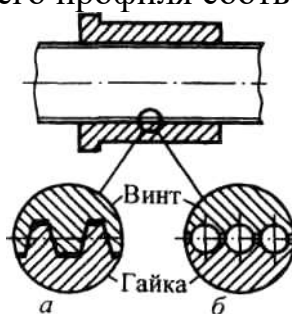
Передача винт-гайка: а — скольжения; б — качения
